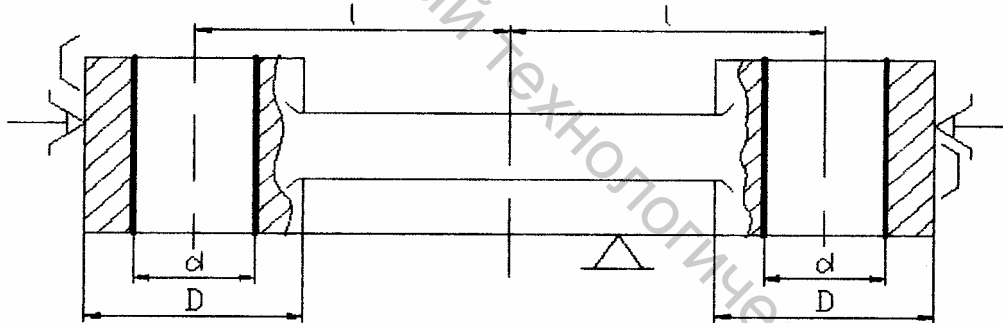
Схема установки заготовки в самоцентрирующих тисках с призматическими губками
